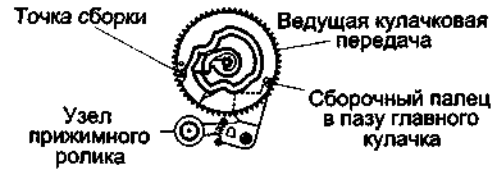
Расположение ведущей кулачковой передачи и прижимного ролика
